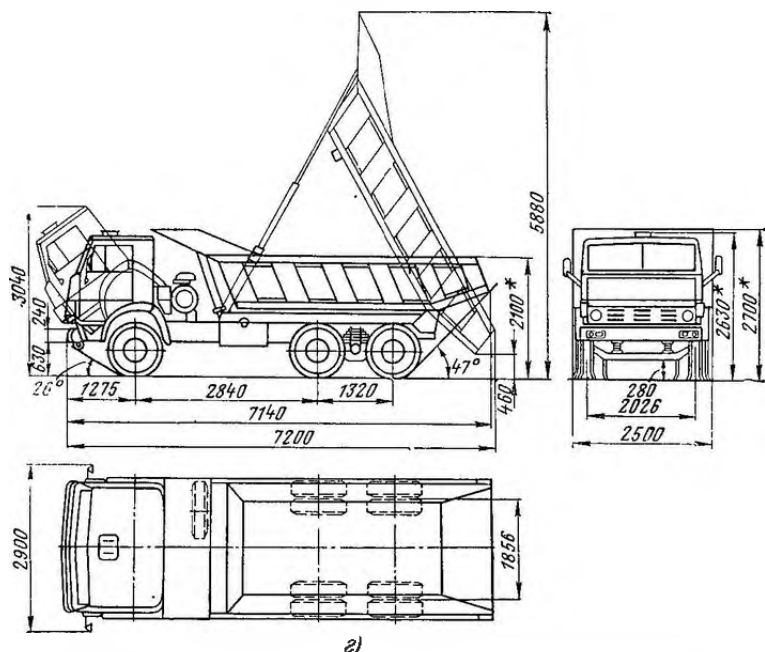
с — автомобиля-самосвала КамАЗ-5511 (размеры даны для автомобиля полной массы, размеры со звездочкой — для снаряженного автомобиля)
